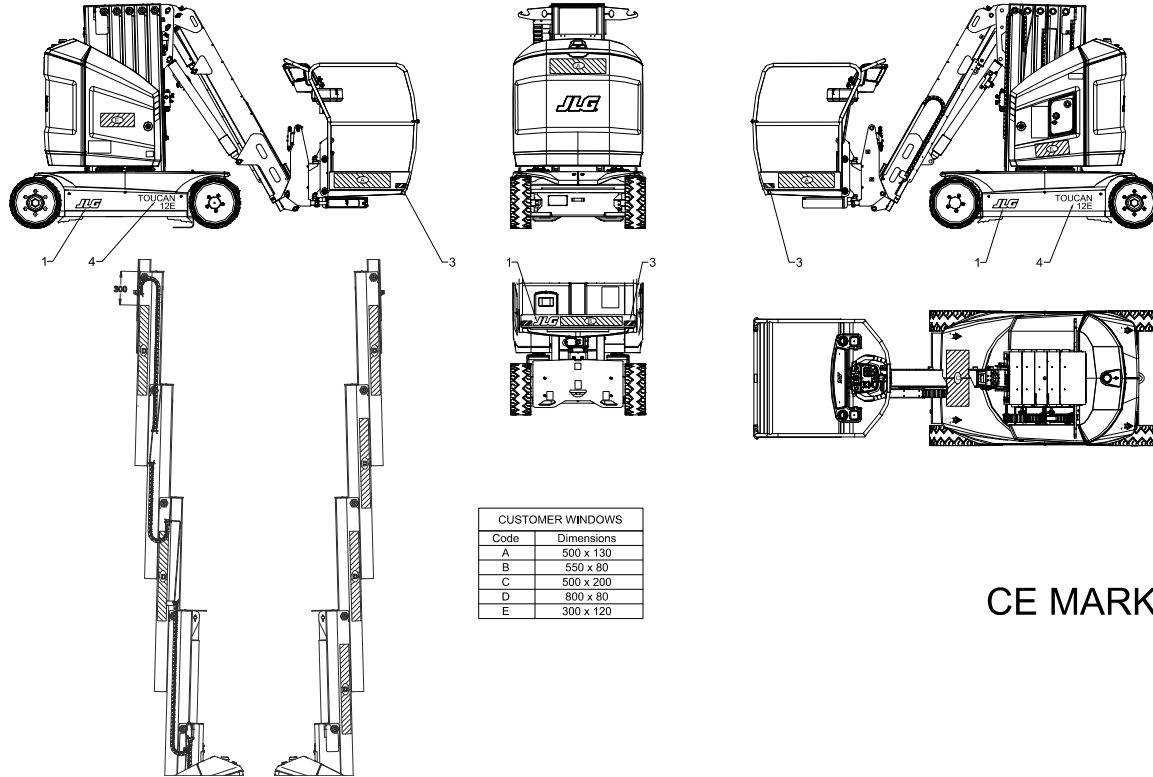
Anbringung der Maschinenaufkleber - Blatt 2
